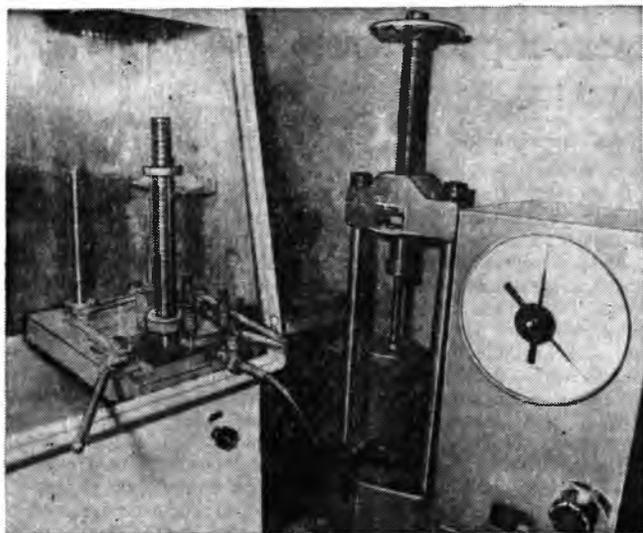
Установка для заполнения подшипников антифрикционным твердосмазочным компаундом
